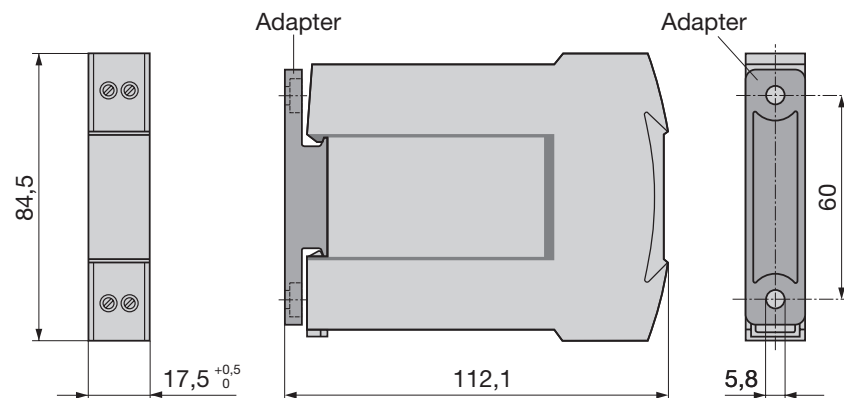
SINEAX SI 815-5.... (N17-Gehäuse) mit Adapter für direkte Wandmontage.
